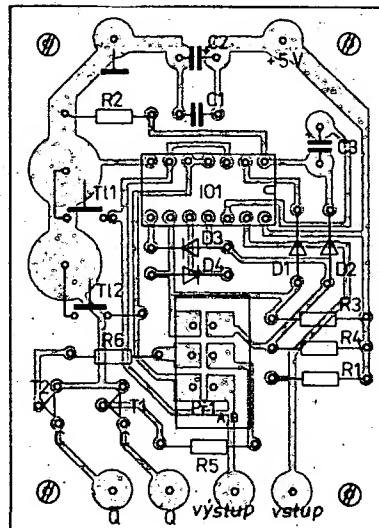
Obrazec plošných spojů pro modul 2 (P52)
